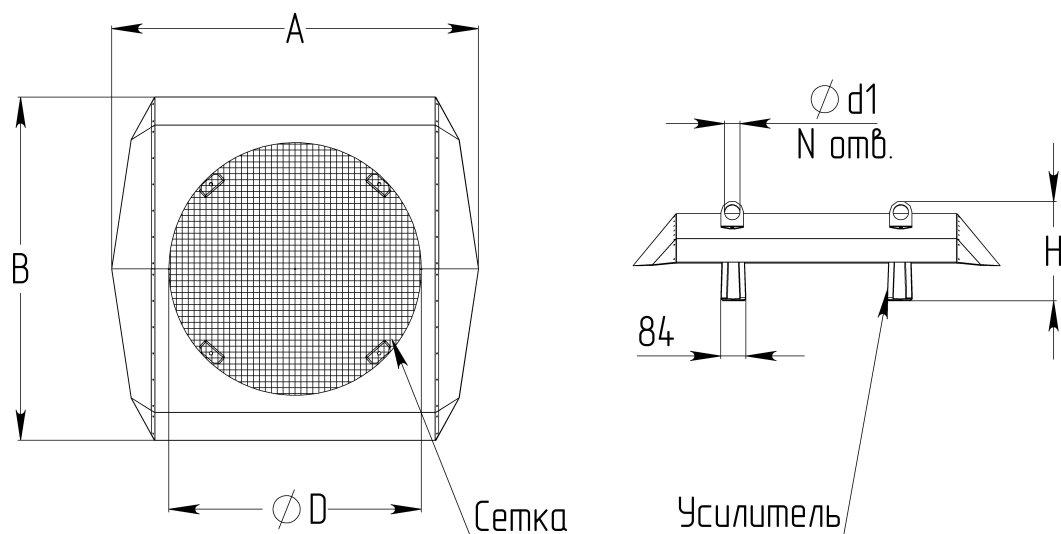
Внешний вид и основные размеры комплекта крыши
